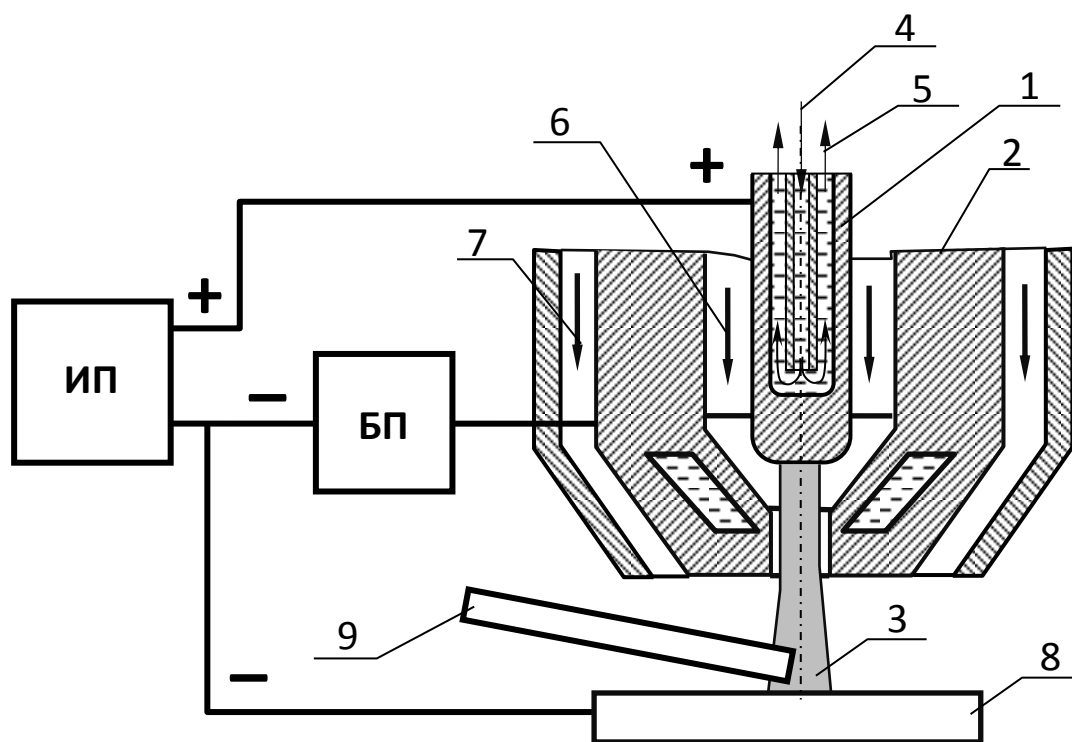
Схема сварки плазменной дугой обратной полярности
